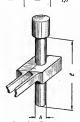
Прокатка заготовки в каталие: — длина прокатываемой части; — конечный диаметр изделяя.
